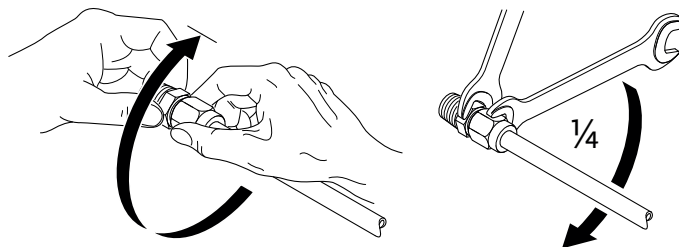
Ruotare ulteriormente il raccordo a compressione di 1/4 di giro
